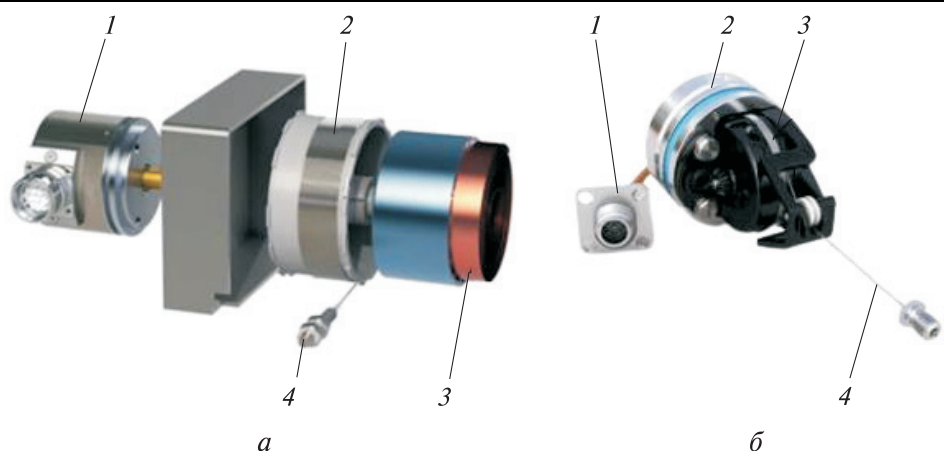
Тросовый измерительный преобразователь линейного перемещения: *а* — тросовый механизм (1 — угловой энкодер; 2 — тросовый барабан; 3 — спиральные пружины; 4 — шарнирный винт); *б* — измерительный преобразователь SGH10 (1 — электрический соединитель; 2 — электронный блок; 3 — тросовый барабан; 4 — тросик)
